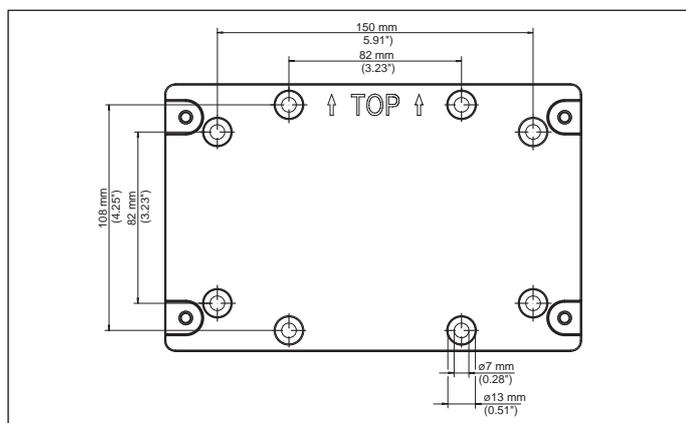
Piastra di montaggio per montaggio a parete (VEGAMET 861, 862)
